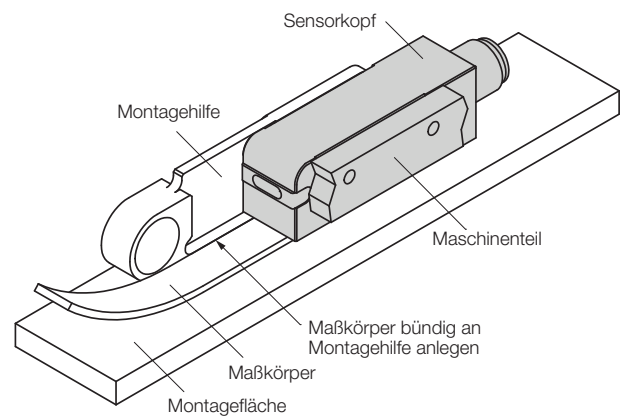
Montagehilfe BAM TO-ML-006-S1G (Bestellcode BAM0256) befestigen (Links- oder rechtsseitige Befestigung ist möglich, Abbildung zeigt rechtsseitige Befestigung)
